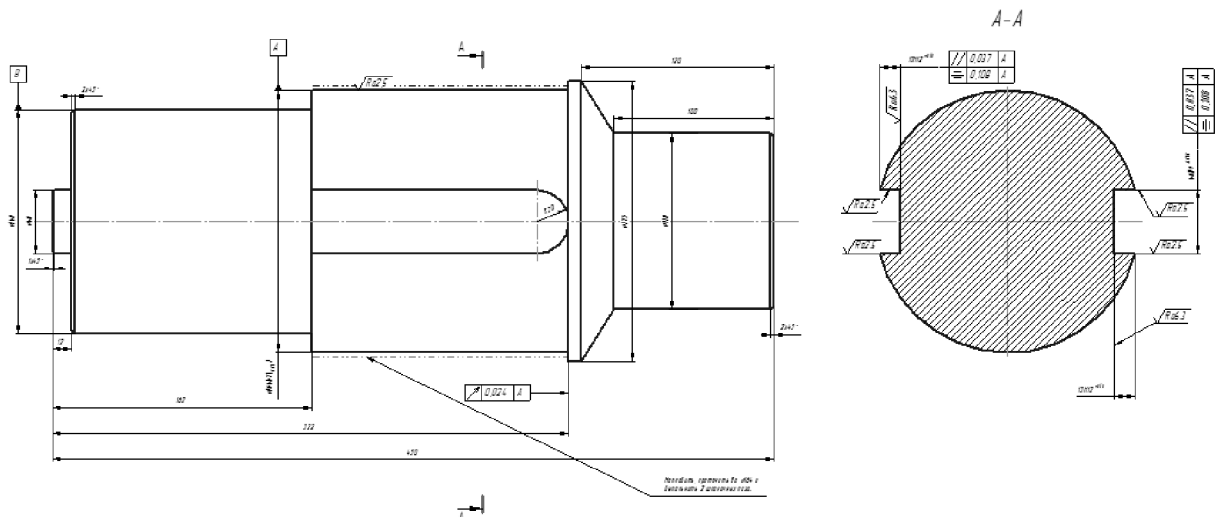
Робоче креслення деталі вал 4-ої передачі редуктора СПЦ26У
